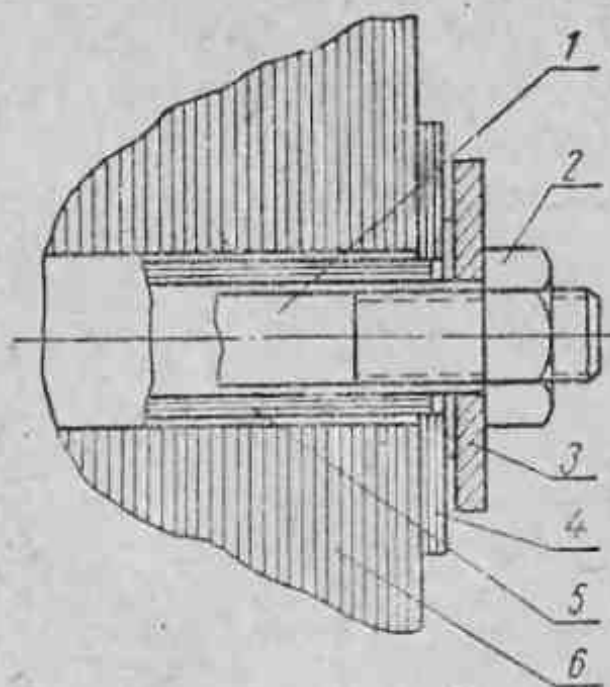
Прессовка стальных листов стержней стяжными шпильками:
